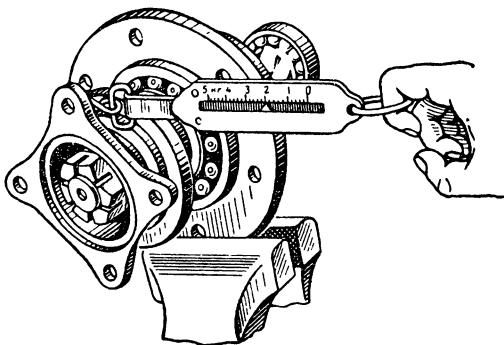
Проверка затяжки подшипников главной передачи при регулировке
